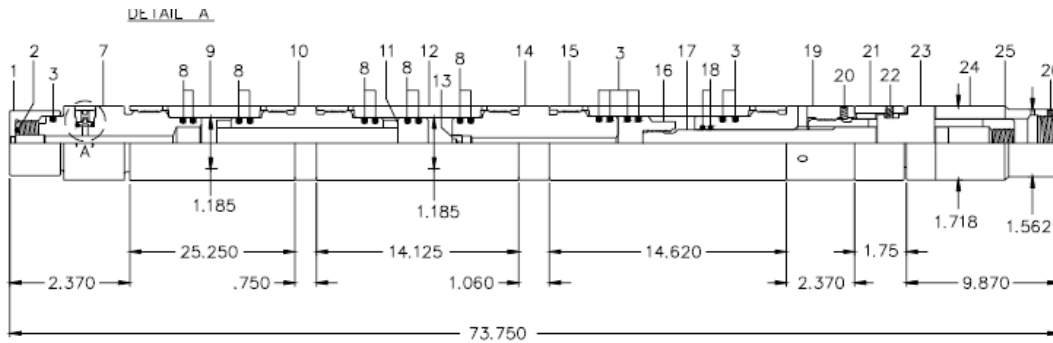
Ensamblaje de la Setting Tool. Baker Hughes Inc.
